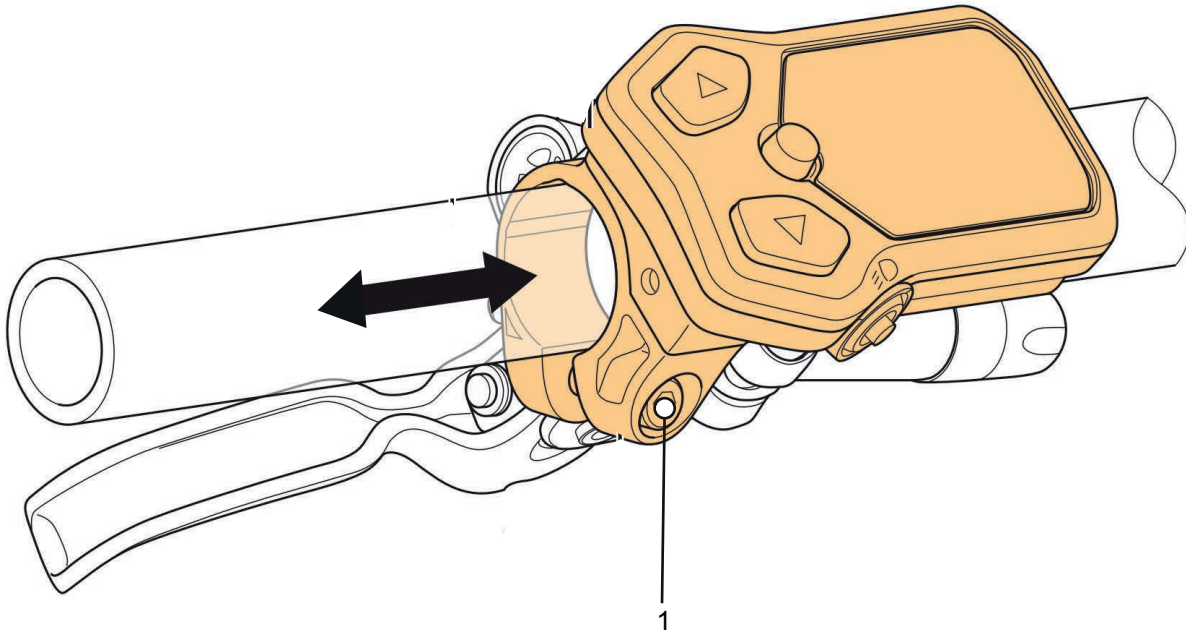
Lage Befestigungsschraube Bordcomputer SC-E5003
